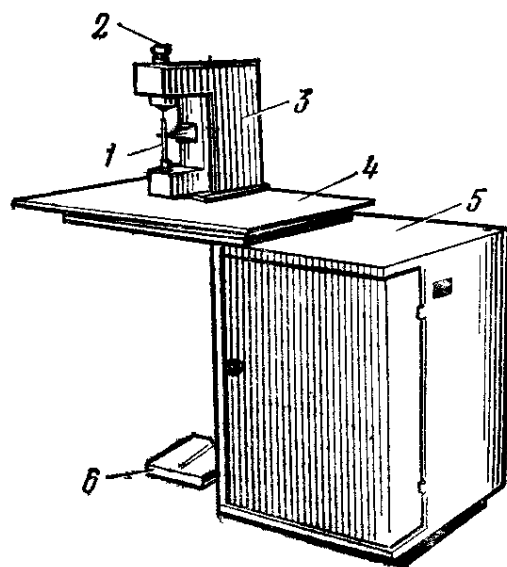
Машина для ультразвуковой сварки МТУ-04-3
